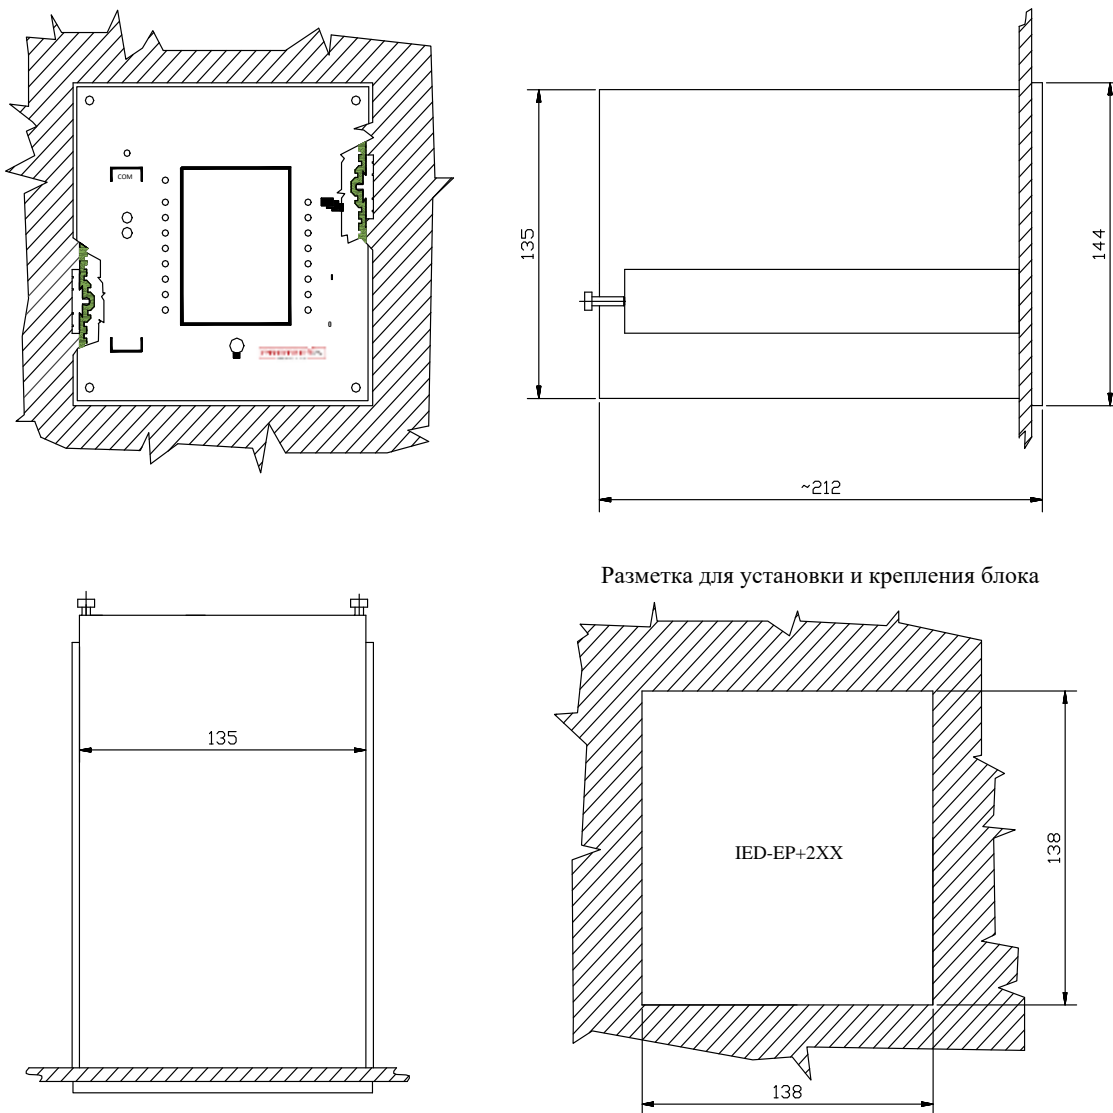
Габаритные, установочные и присоединительные размеры модификации IED-EP+2XX и разметка для монтажа в шкаф
